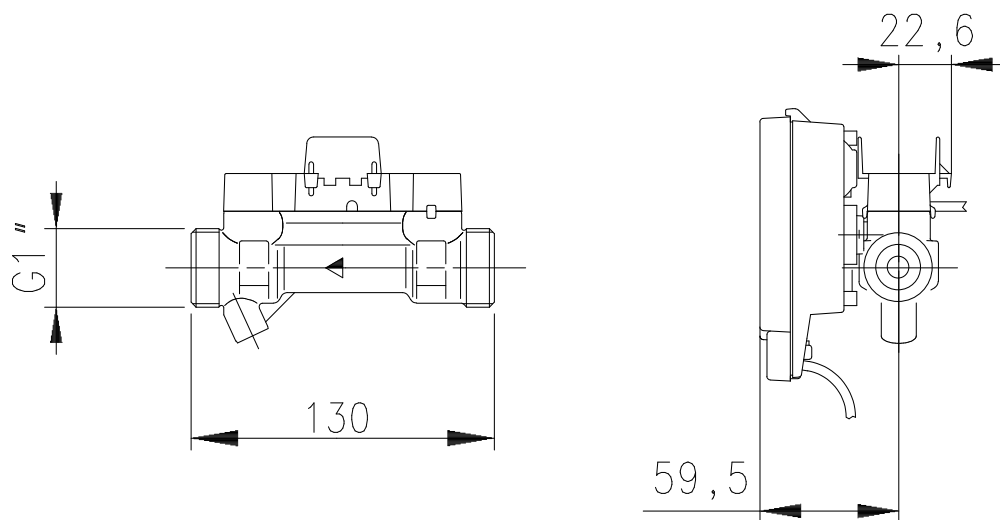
Габаритные и установочные размеры преобразователей расхода «СТРУМЕНЬ» Т150 исполнений: 26U, 36U, 37U
